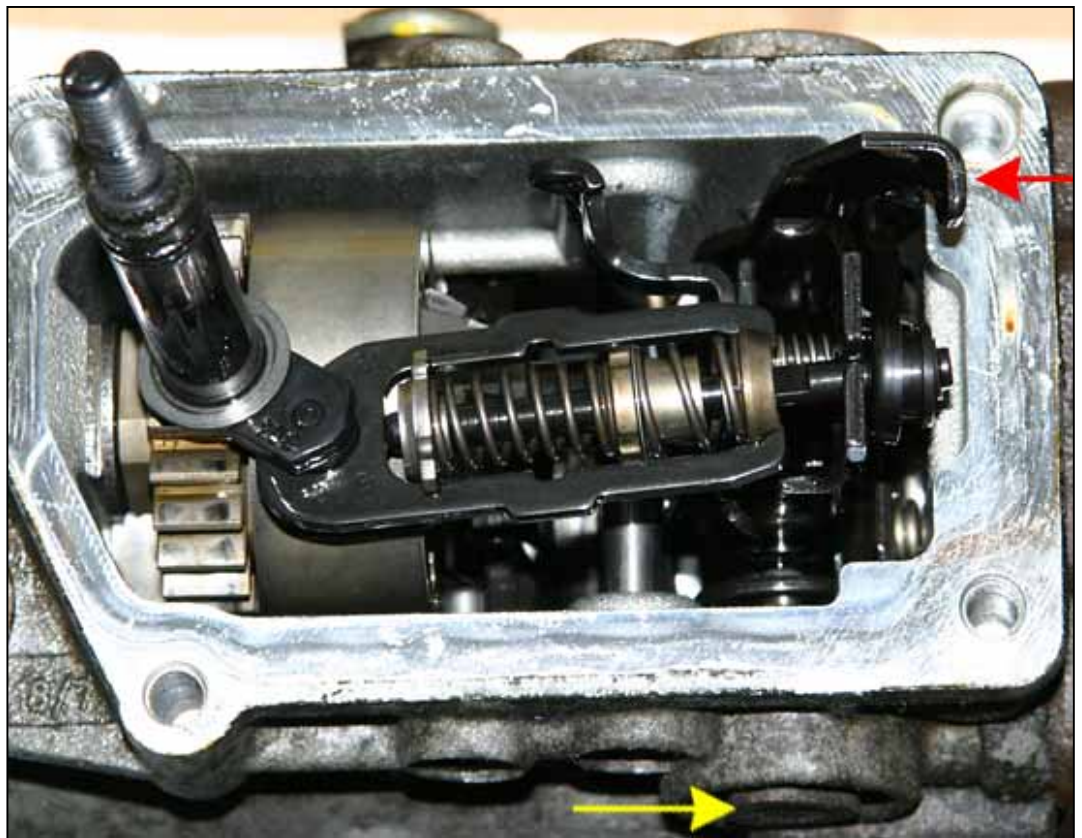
Blick von oben in die offene ESP (Die Fördermengenschraube drückt auf den Hebel oben)
